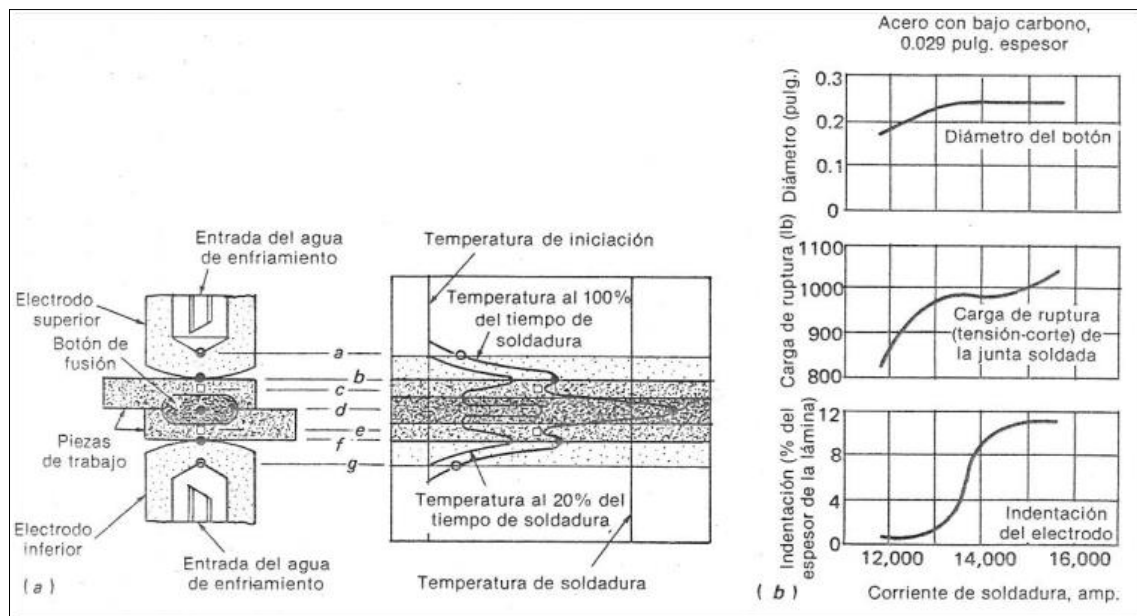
a) Puntos más importantes de generación de calor en soldadura de puntos por resistencia. b) Efectos de la corriente de soldadura en el diámetro del botón fundido, la resistencia a la tensión y al corte, y la indentación del electrodo en la soldadura de puntos por resistencia.
